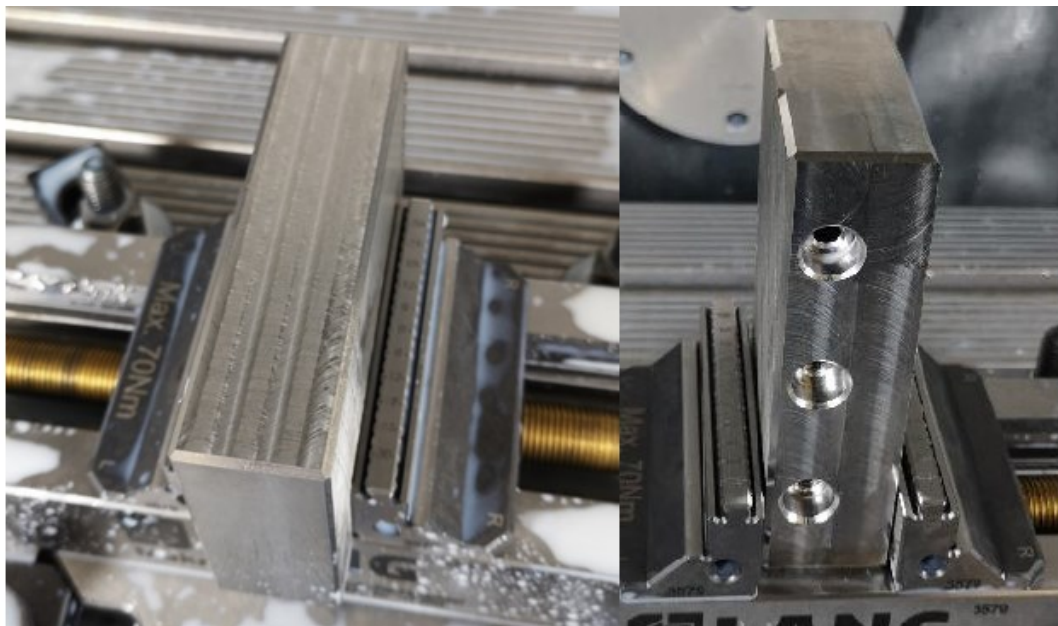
Zkracování polotovaru před výrobou na CNC frézce
